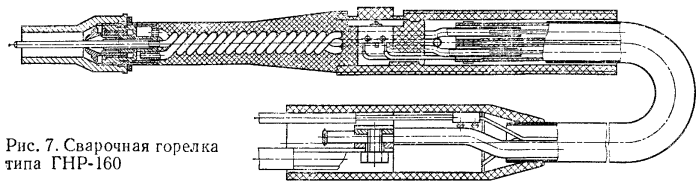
Сварочная горелка типа ГНР-160
